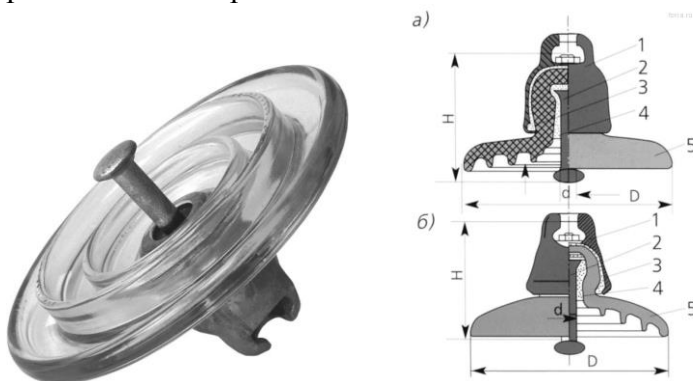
Подвесные изоляторы тарельчатого типа: а – фарфоровый; б- стеклянный; 1 – место крепления; 2 – стержень; 3 – металлическая арматура; 4 – цементный раствор; 5 – изолирующая деталь (стеклянная, фарфоровая)
